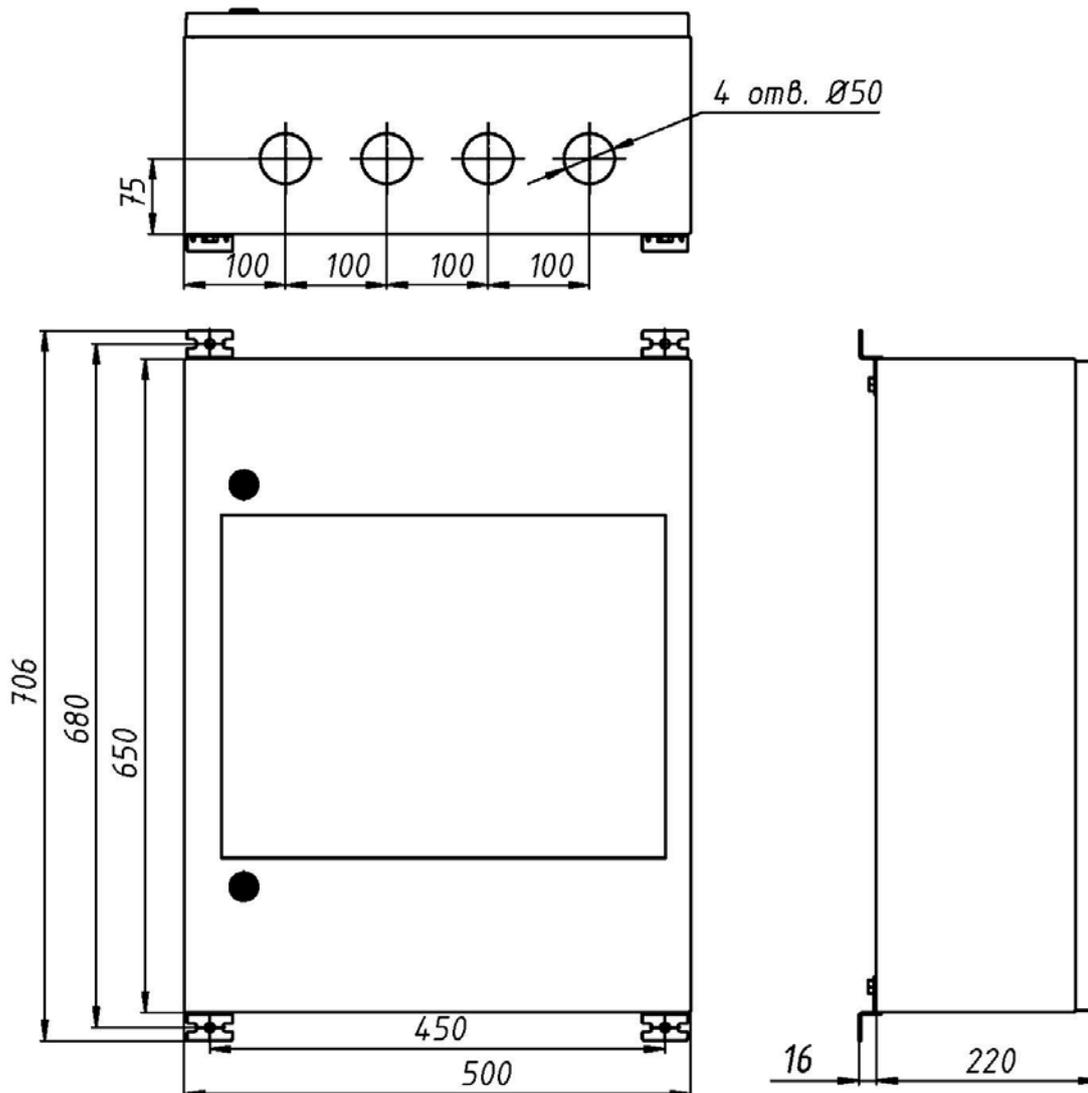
Габаритные размеры корпуса ППО «Эгида»
